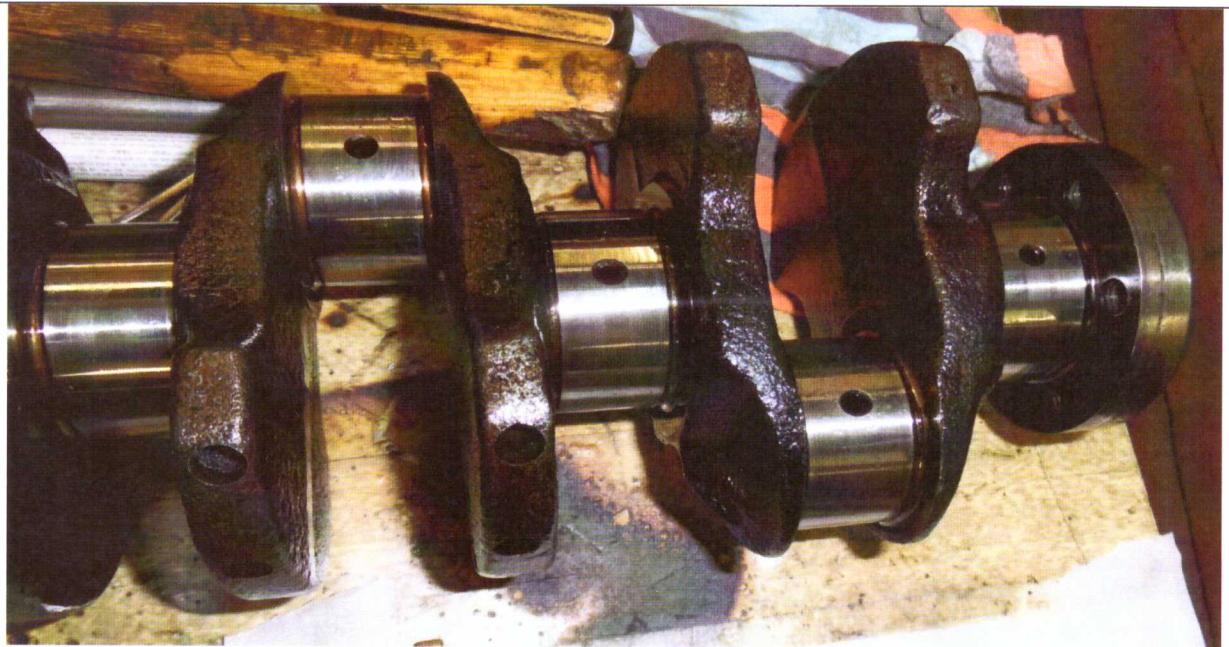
Общий вид шеек коленчатого вала двигателя после аварийного цикла испытаний. Двигатель, обработанный нанокомпозитом Amortect PROOF.
